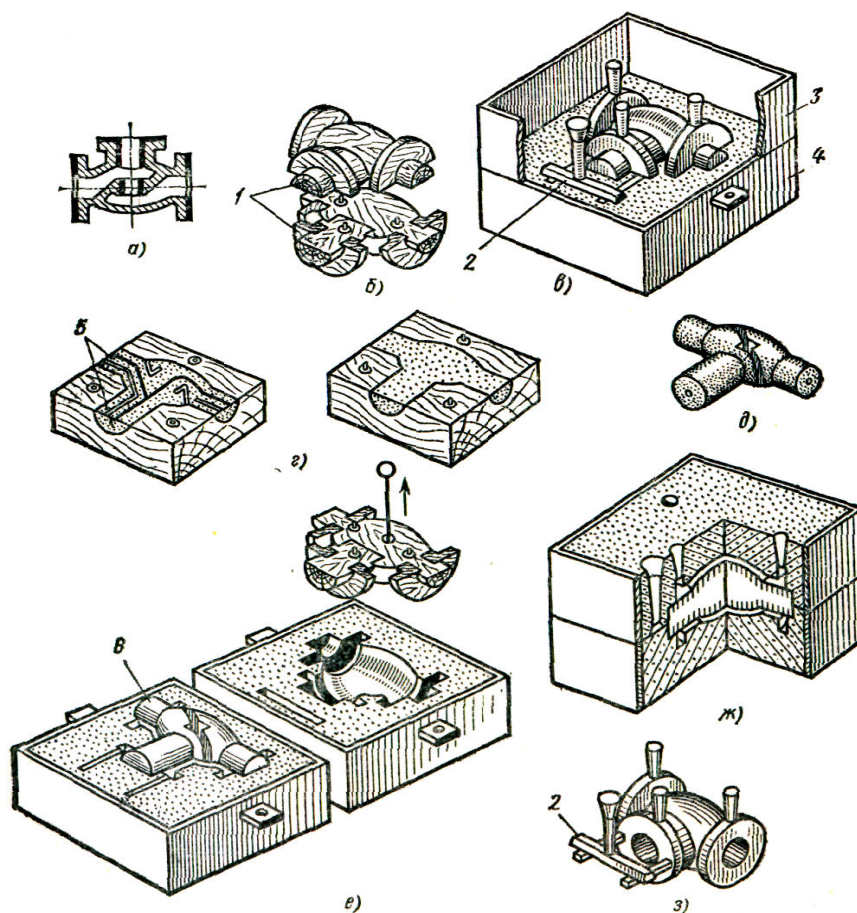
Деталь (а), виготовлення форми (б-ж), виливок (з)
